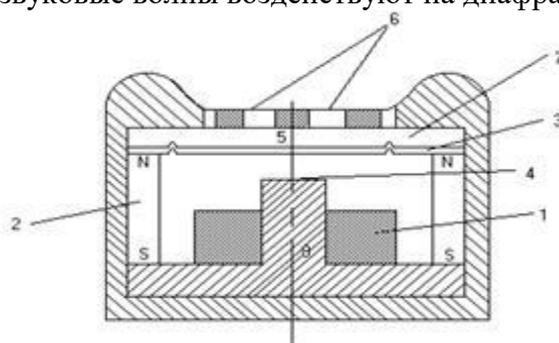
Электромагнитный микрофон конструкции приемника давления
